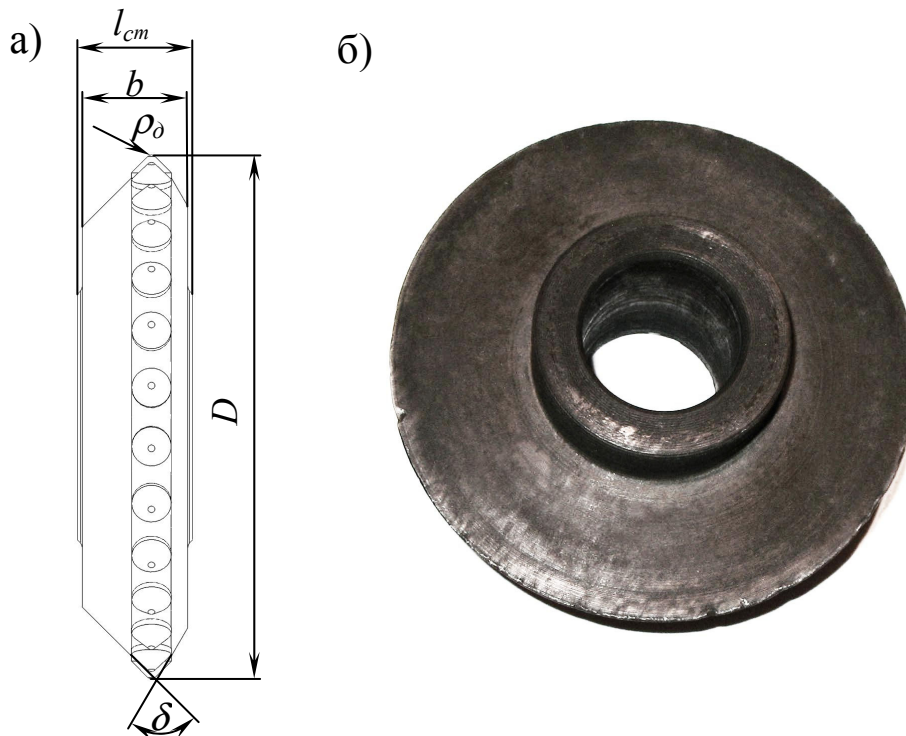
Конструкция (а) и характерный вид износа (б) режущего инструмента с вращающейся режущей частью
